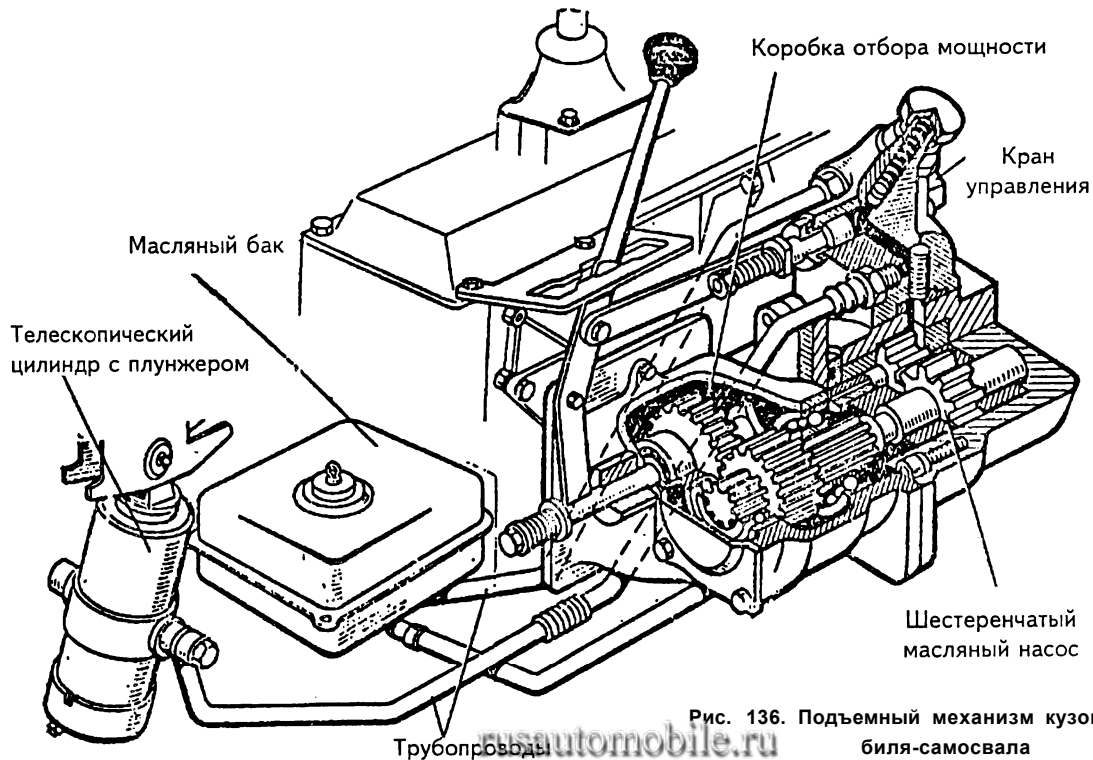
Подъемный механизм кузова автомобиля-самосвала
